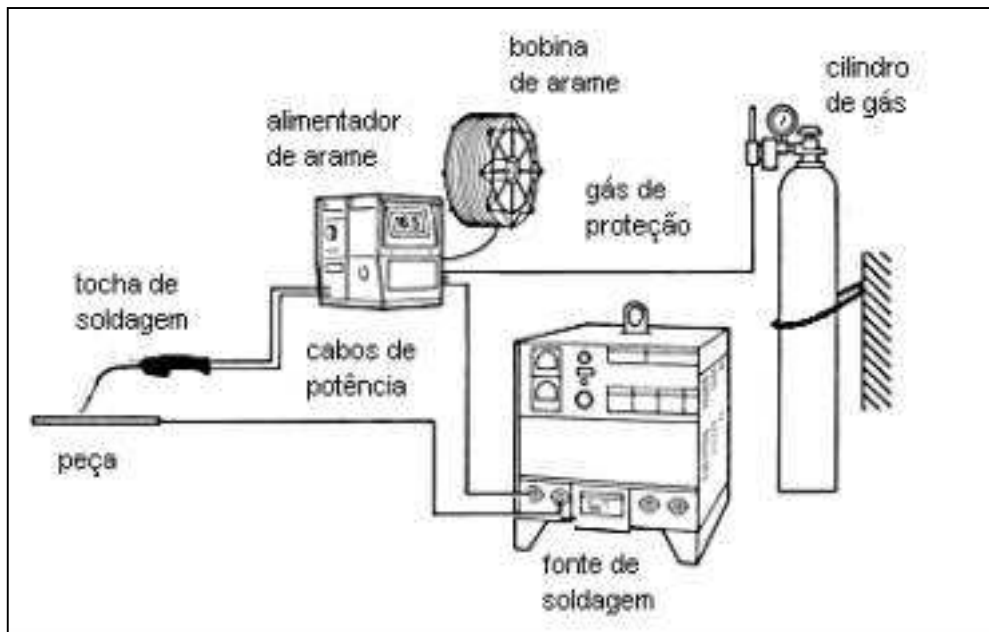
Esquema do processo de soldagem MIG (Metal Inert Gas)
